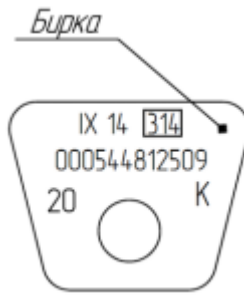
Бирка буксового узла с подшипником кассетного типа в габаритных размерах 130x250x160 торговой марки SKF
